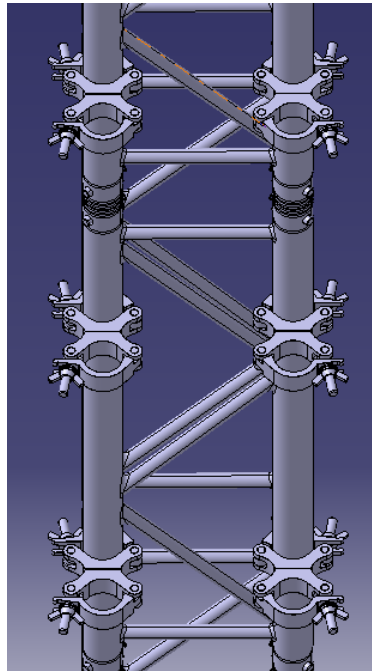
Vista detalle de la disposición de las abrazaderas dobles.
